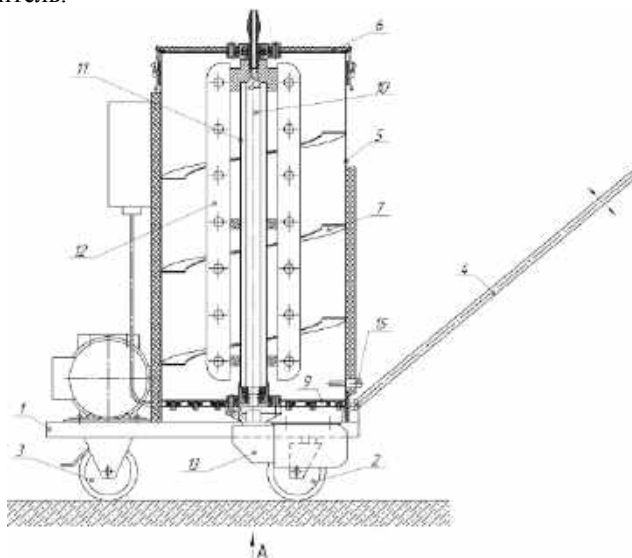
Установка для приготовления и нанесения защитных составов:
